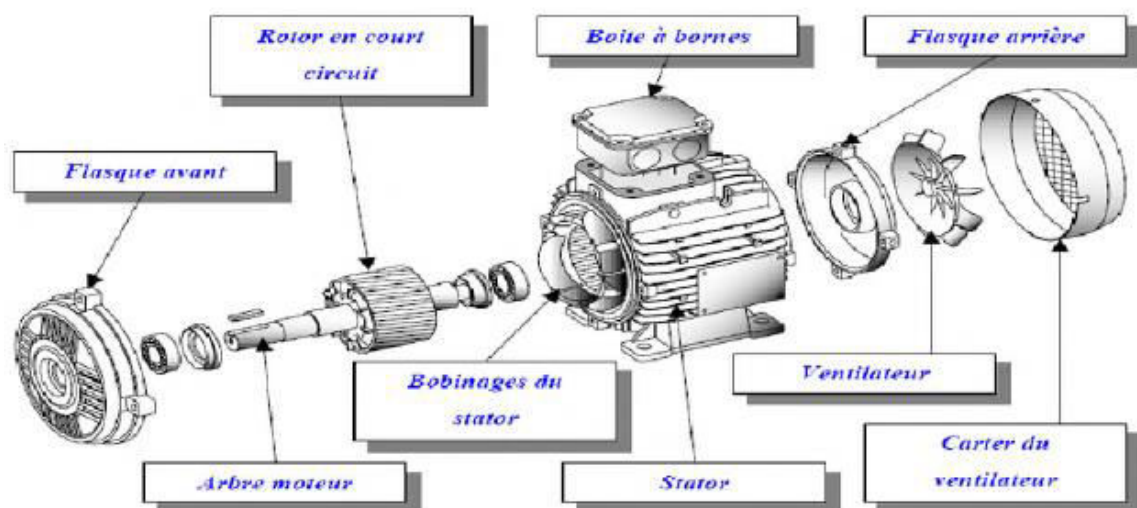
Vue en éclaté de la machine asynchrone [ARK 17]
